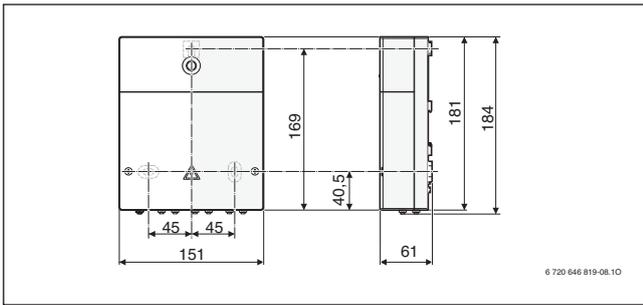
Abmessungen Solarmodul SM100 (Maße in mm)
